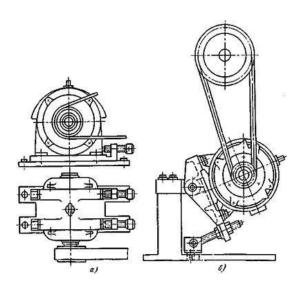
Регулировка натяжения ремня перемещением двигателя: 1 — ремень; 2 — шкив; 3 — натяжное устройство Способы регулирования натяжения ремней установки электродвигателя a) на салазках;  $\delta$ ) на шарнирной плите
